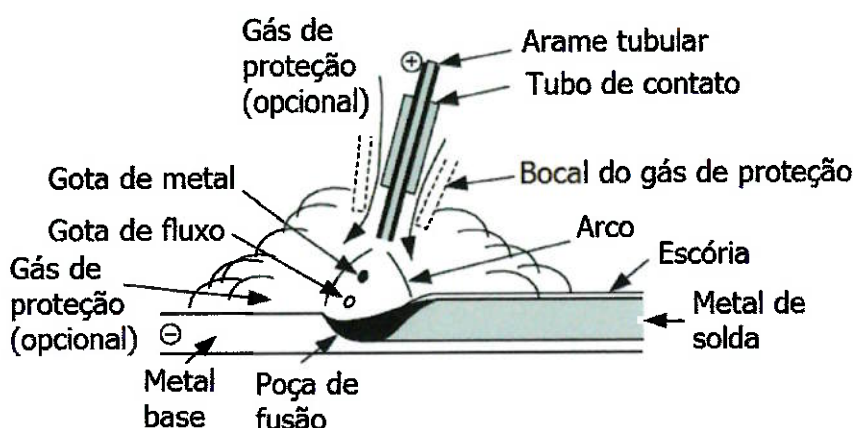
Processo de soldagem ao arco com arames tubulares [7, adaptado]
